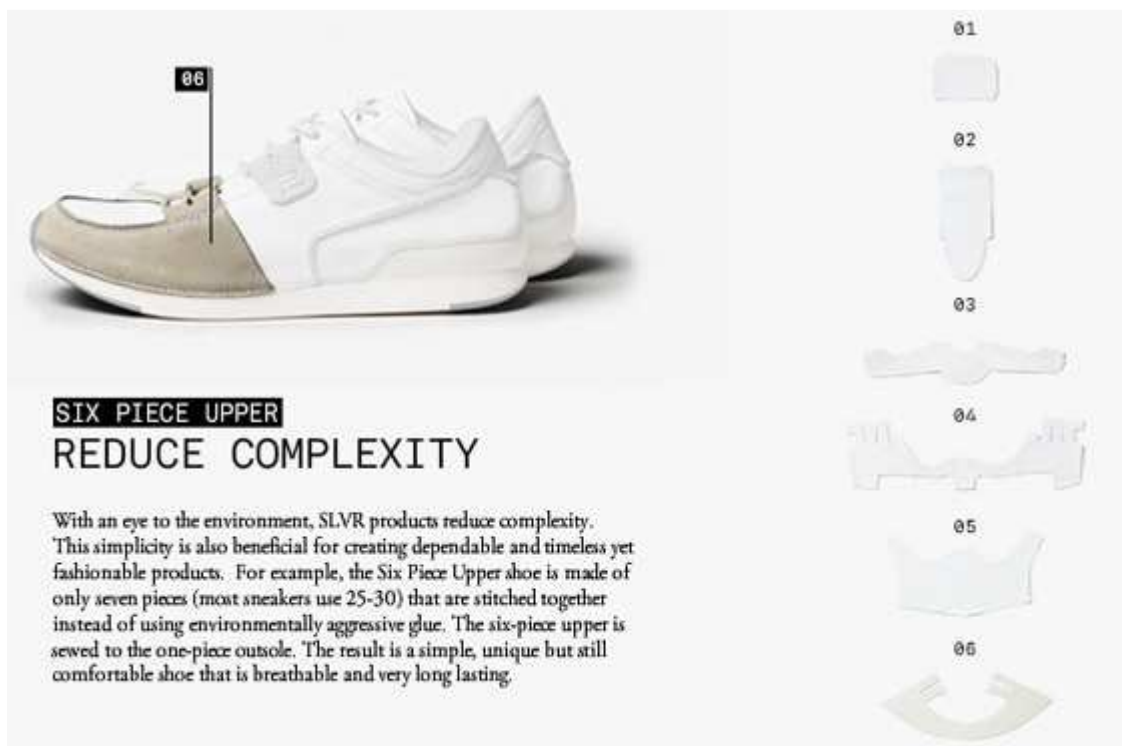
Construção da sapatilha Six Piece Upper ADIDAS
